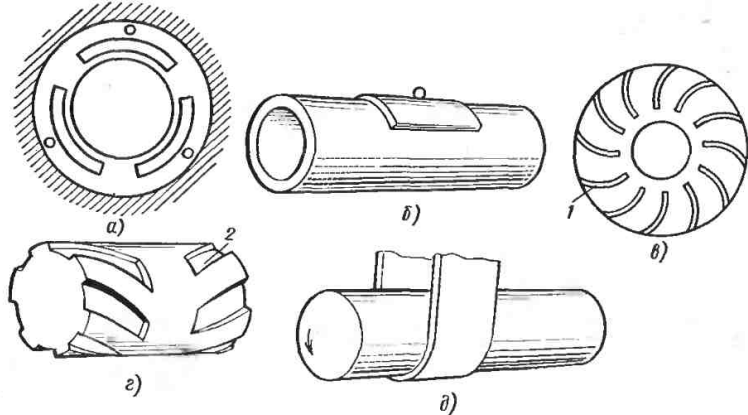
Газодинамические подшипники: а, б — с подвижными вкладышами; в — упорный со спиральными канавками 1; г — радиальный со спиральными канавками 2; д — пленочный
